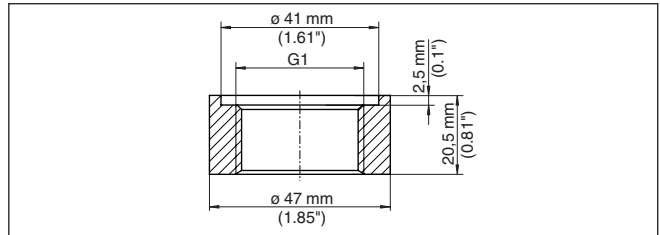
Maße Einschweißstutzen Gewinde G1 (DIN 3852-X)
